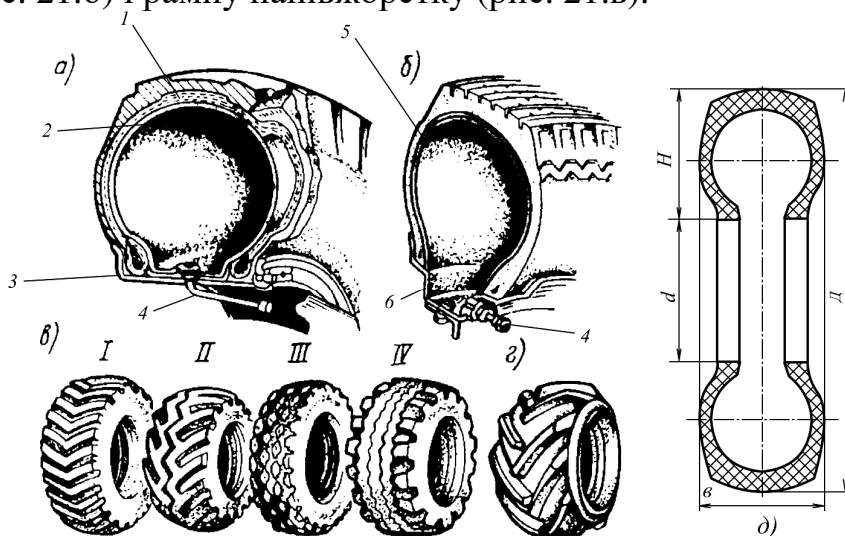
Шини: а - камерні; б - безкамерні; в - типи протекторів; г - арочні шини; д - основні розміри шини; 1 -
